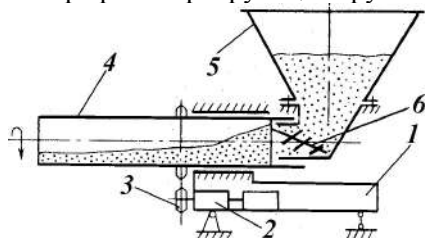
Трубчатый питатель с неподвижным бункером:
